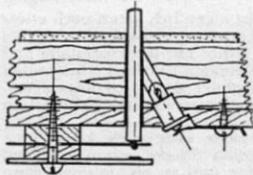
Schnitt quer zu einem Kanal in Höhe einer Signaldrucktaste (mit der Drucktastenbeleuchtung durch schräggestellte Lämpchen).
